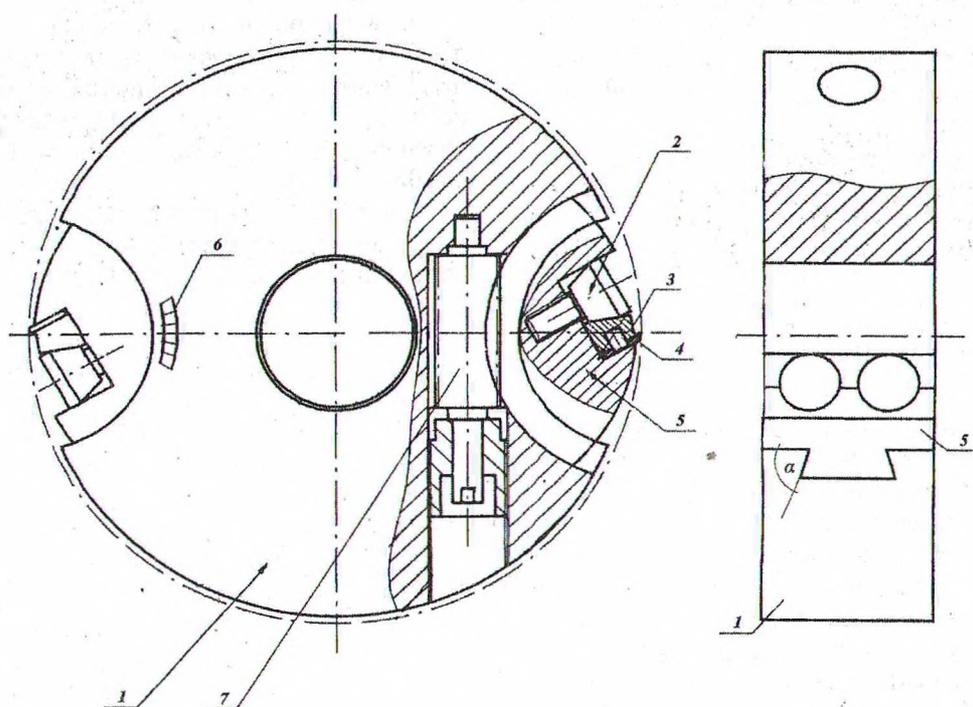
Сборная фреза с поворотными ножедержателями и устройством для позиционирования: 1 – корпус фрезы; 2 – винт; 3 – клин; 4 – нож; 5 – сегмент-ножедержатель; 6 – шкала для настройки угла резания; 7 – червяк
